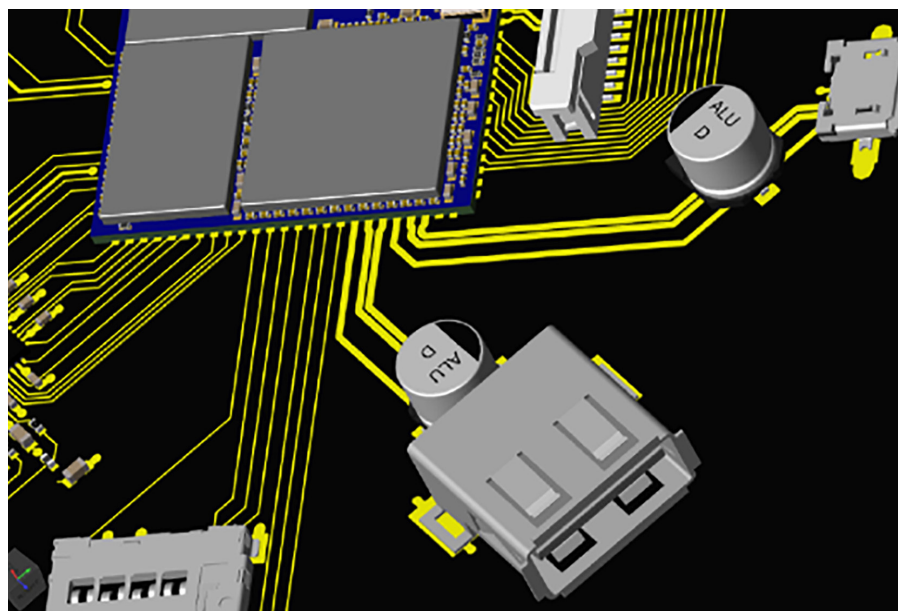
Pad GND oraz rozstaw pinów modułów rodziny QS
